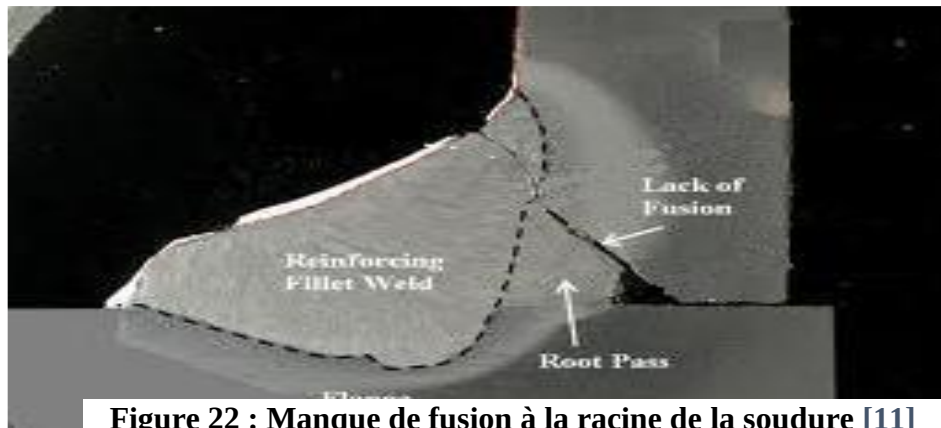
Manque de fusion à la racine de la soudure [11]
